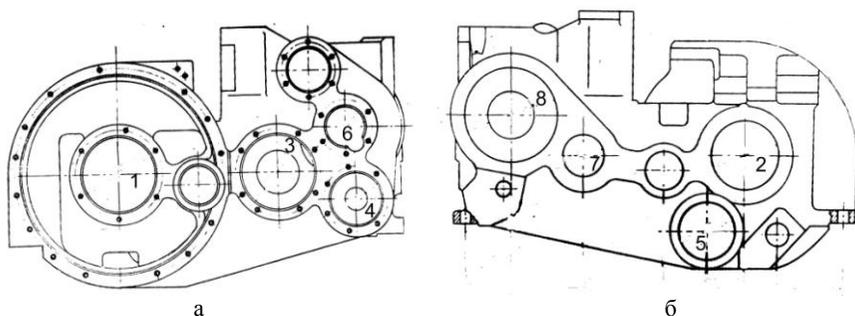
Эскиз корпуса редуктора из сплава АК6Мг:
